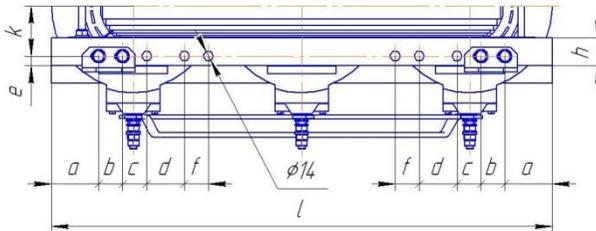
в – Присоединительные размеры трансформатора (вид сверху).
